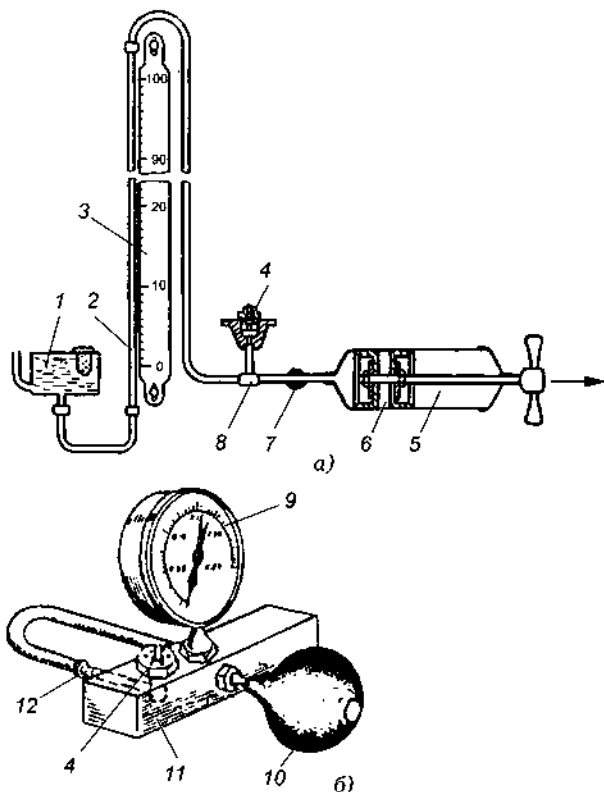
Приборы для проверки герметичности игольчатого клапана: *а* — стационарный; *б* — переносной; 1 — бачок; 2 — трубка; 3 — шкала; 4 — клапан; 5 — ручной насос; 6 — поршень; 7 — краник; 8 — тройник; 9 — манометр; 10 — резиновая груша; 11 — камера; 12 — трубопровод
